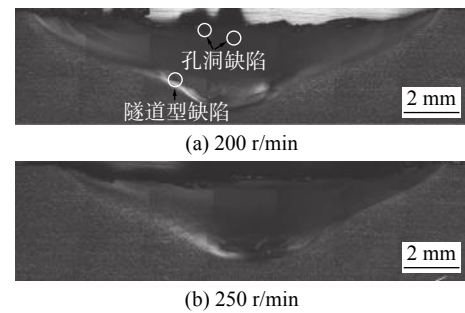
不同焊接工艺条件下的 FSW 接头横截面形貌
